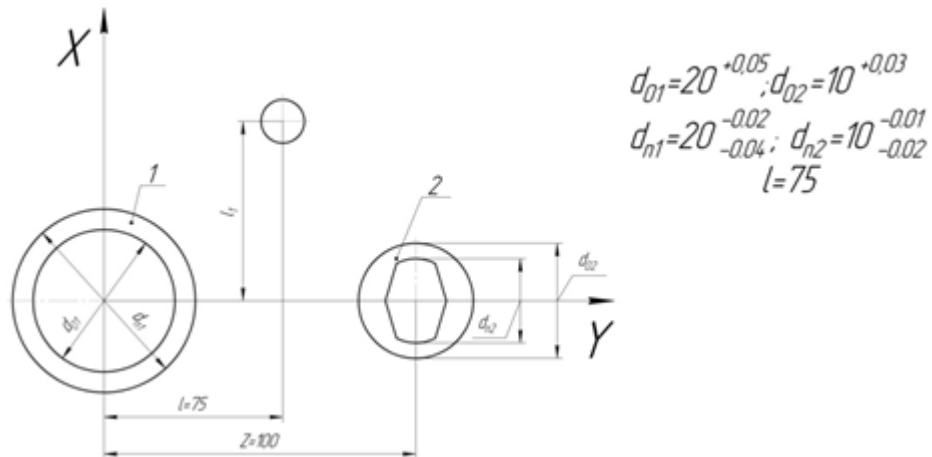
Схема установки детали в приспособлении к заданию 11
